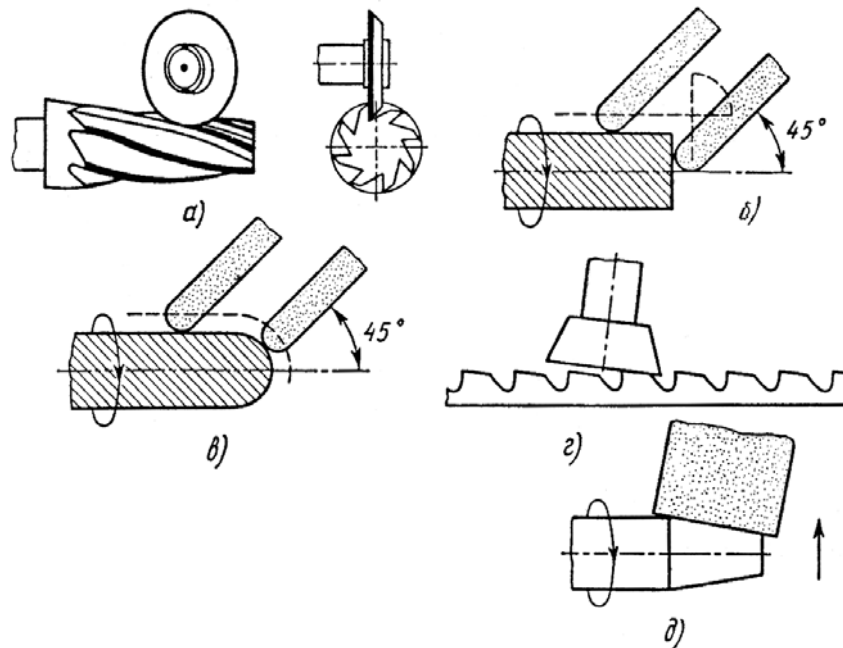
Схемы заточки на заточном станке с ЧПУ многолезвийного инструмента:
